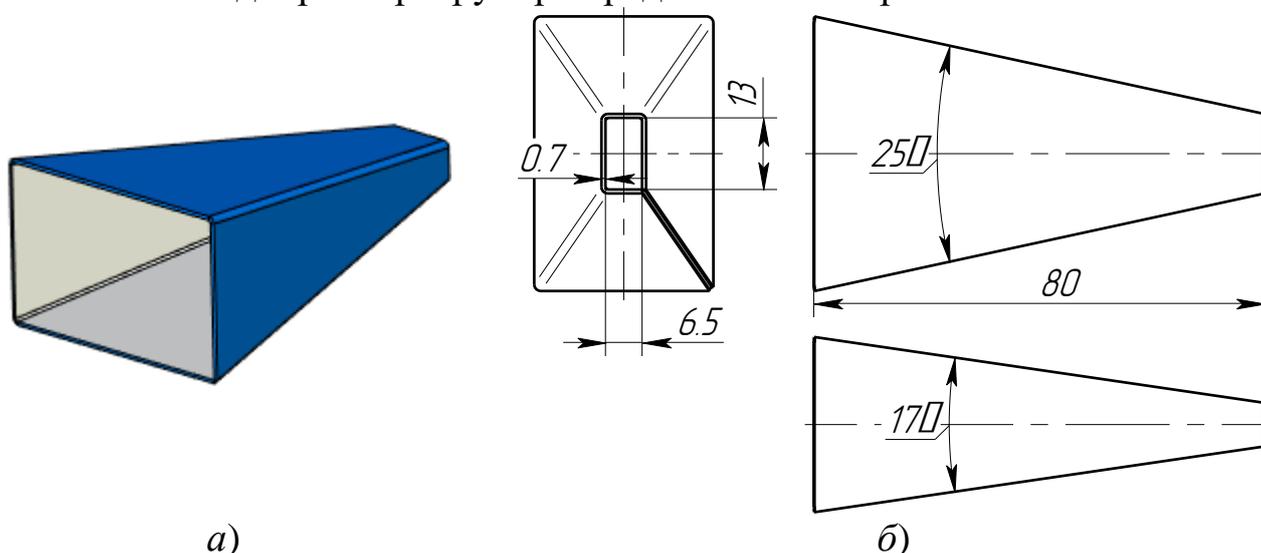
Рупор: *a* – внешний вид; *б* – размеры
